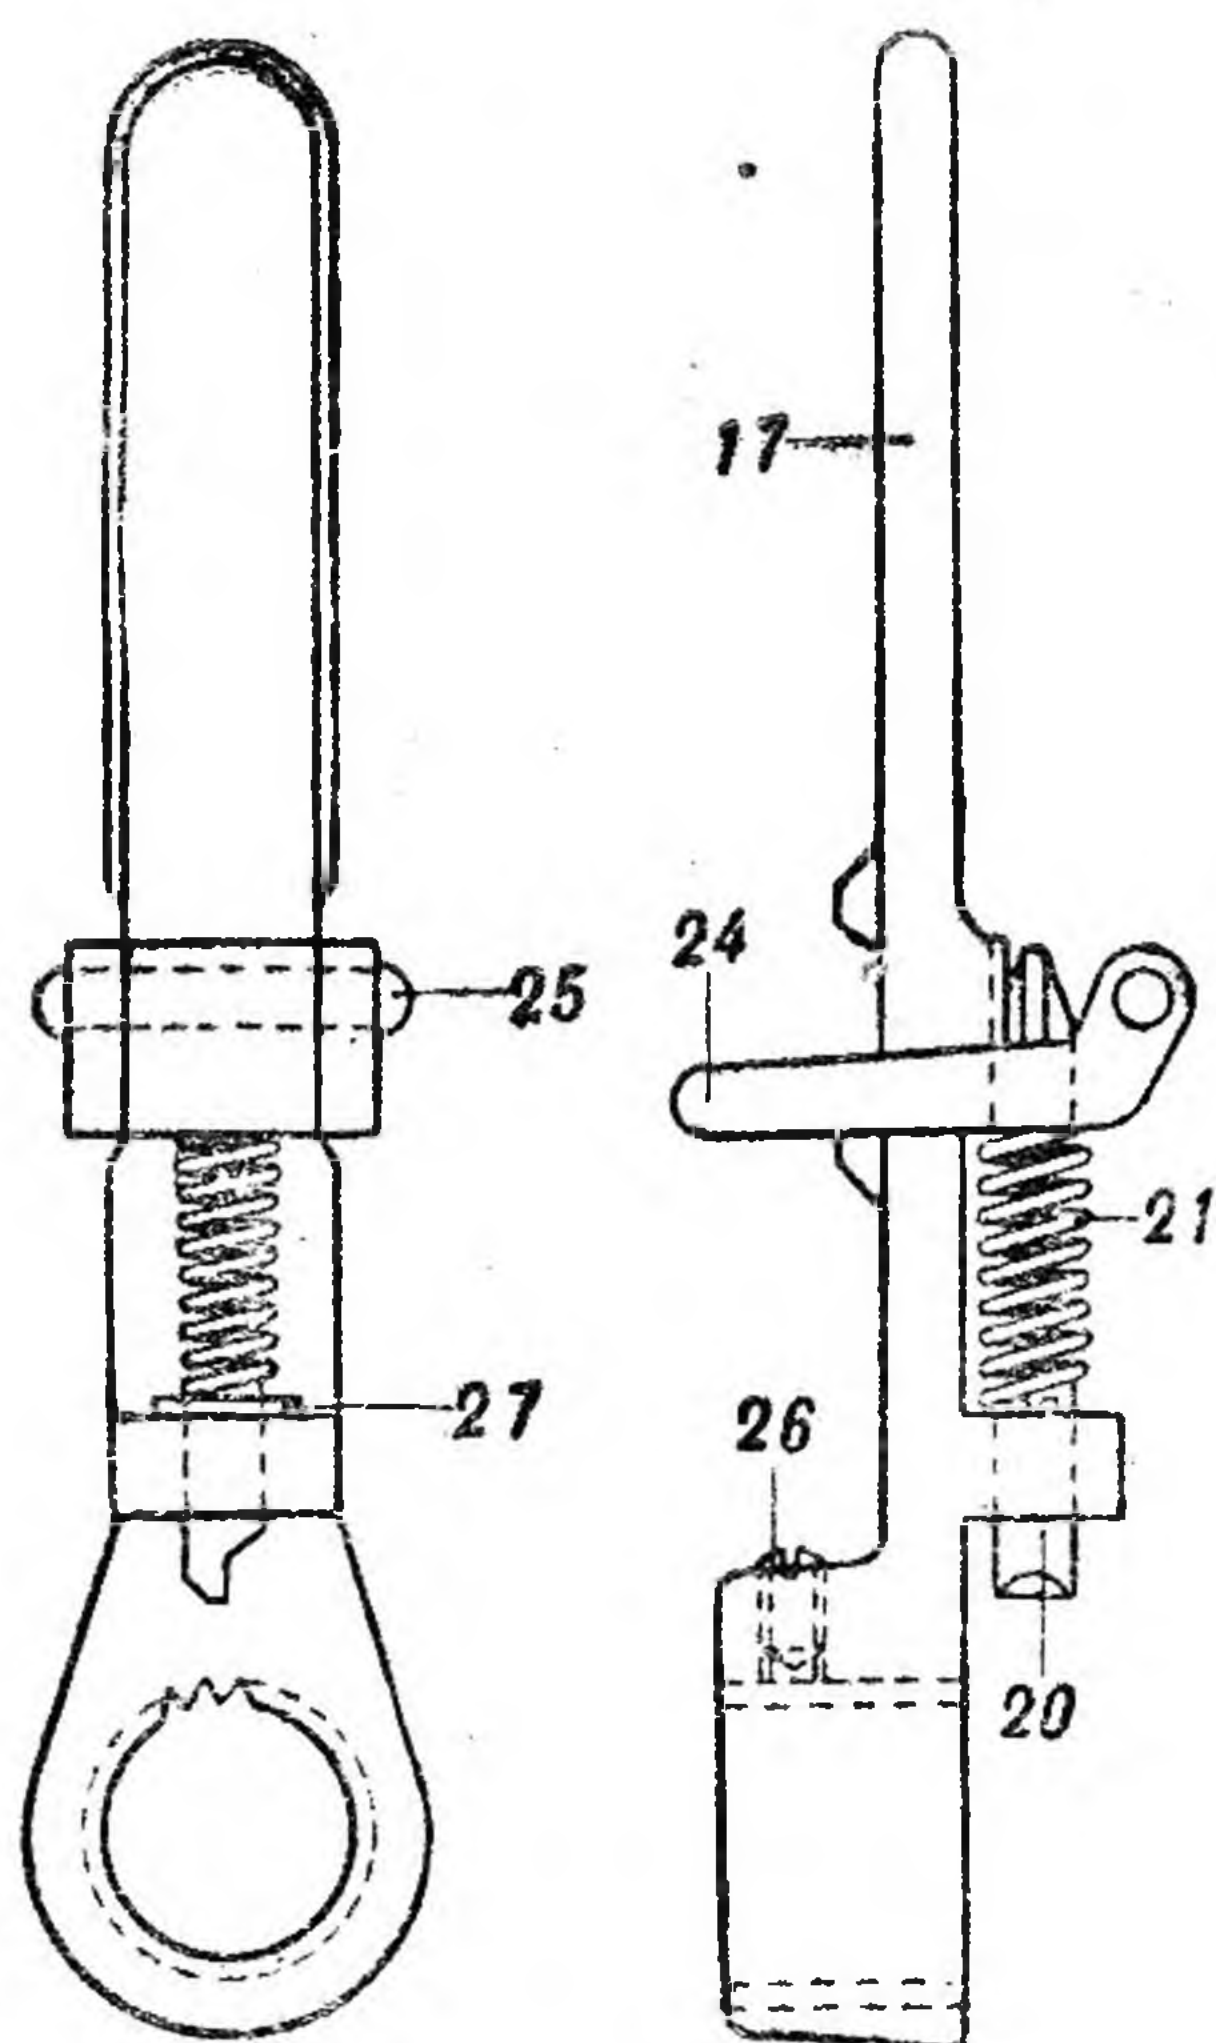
Рукоятка стопора походного крепления верхнего станка на нижнем
